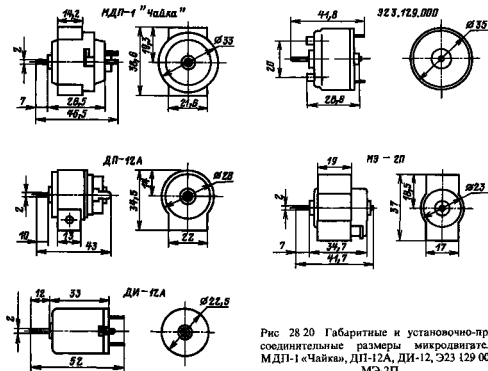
20 Габаритные и установочно-присоединительные размеры микродвигателя МДП-1 «Чайка», ДП-12А, ДИ-12, Э23 129 000, МЭ-2П
